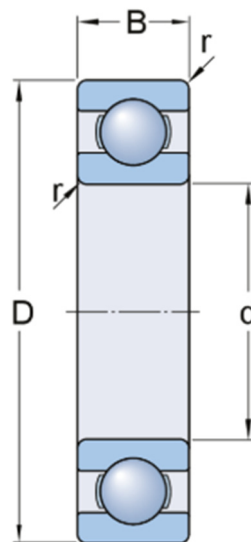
Dimensioni di ingombro di un cuscinetto
